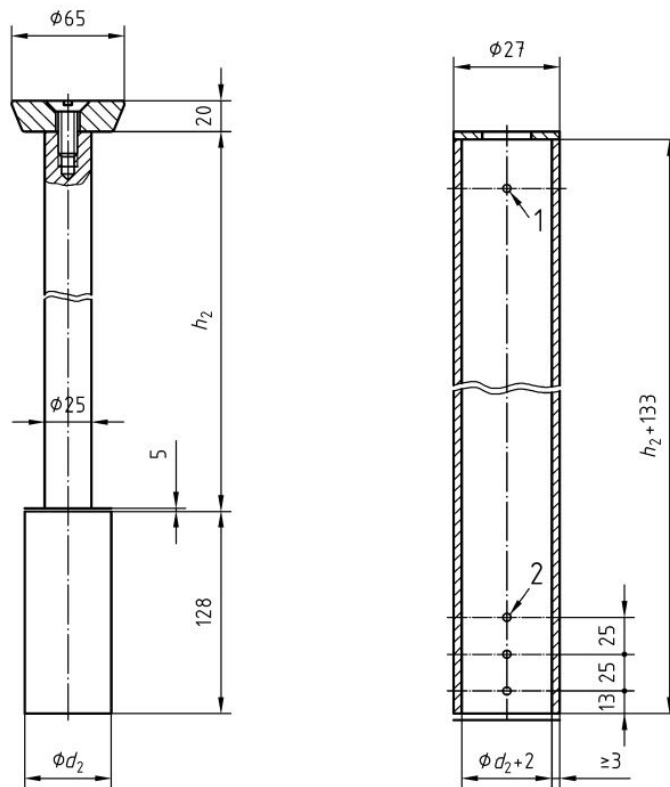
Prinzipskizze Proctorhammer mit Führung, Quelle: DIN EN 13286-2:2013-02 [23]
